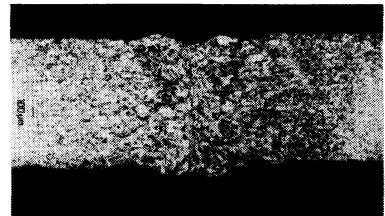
Innenblech A-Säule; Außenkontur Radius 5mm; I-Naht am Stumpfstoß; Prozeßführungsstrategie Linearisierung
